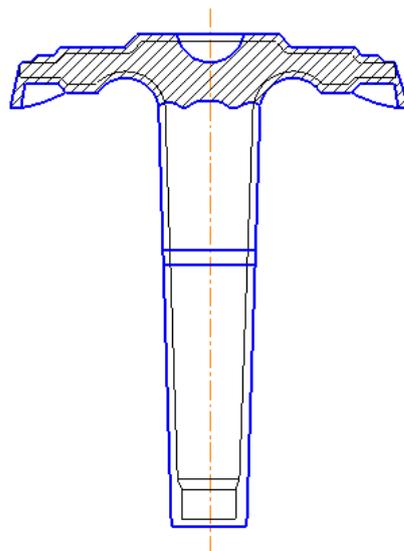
Поковка вала-муфты сцепления, полученная на молоте
